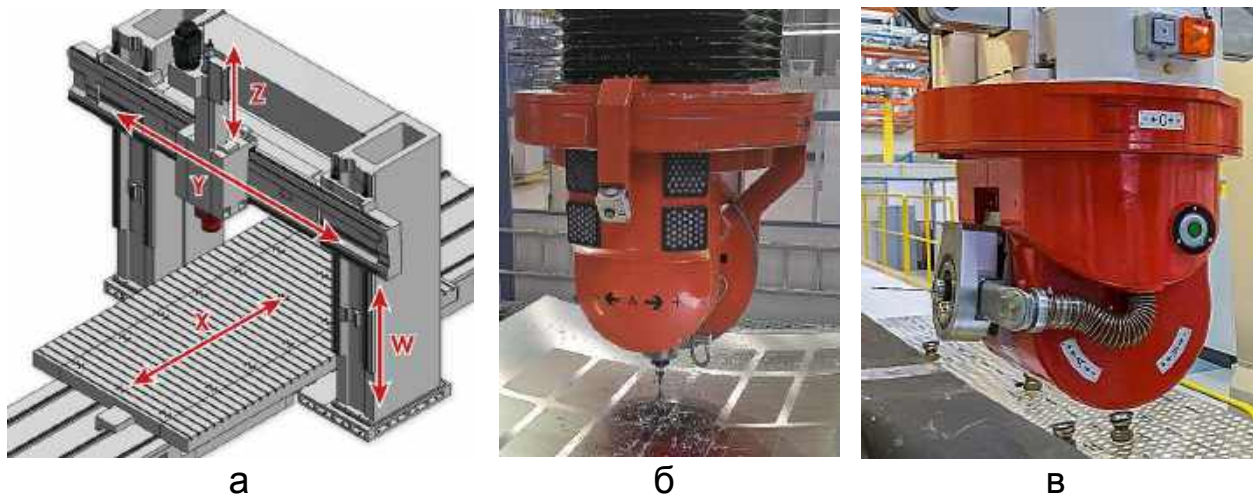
Схема позначення координат (а) і загальний вигляд двокоординатного шпindelъ (б, в) портального фрезерного верстата
